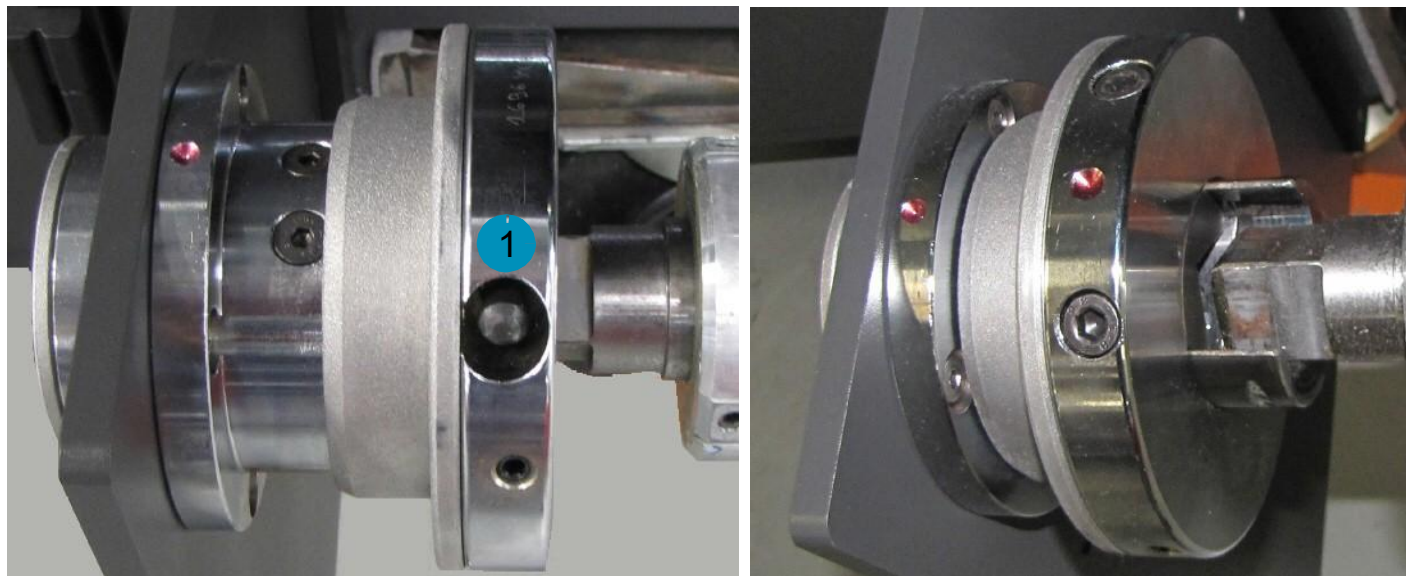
Закрытый фиксатор вала (слева) и открытый (справа)
